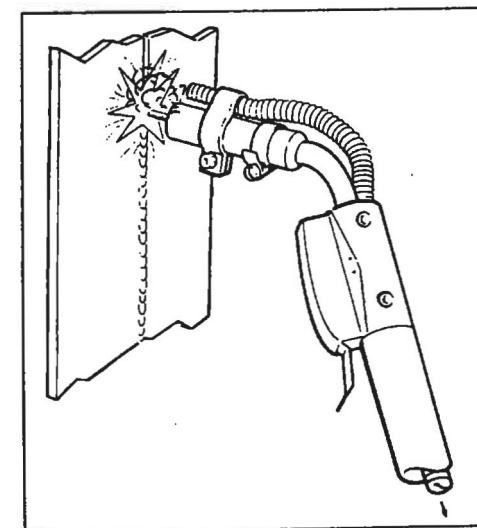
PISTOLA DE SOLDEO CON EXTRACTOR
